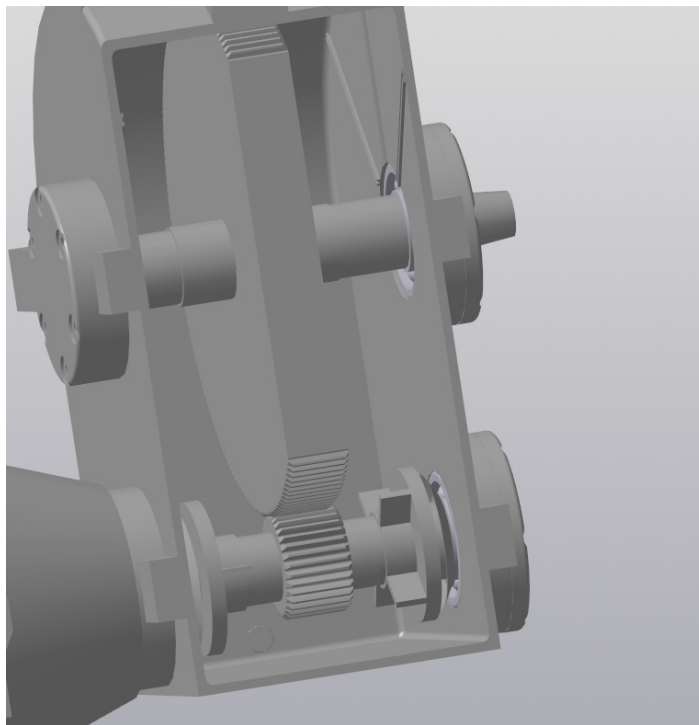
Цилиндрический одноступенчатый редуктор с нижним расположением быстроходного вала
